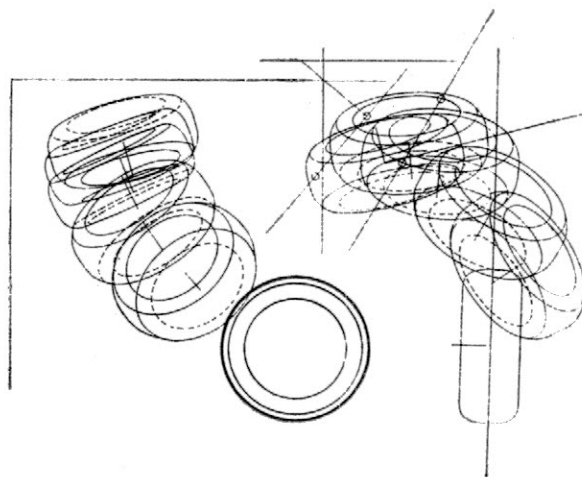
Кинематика колеса основной стойки шасси при уборке
